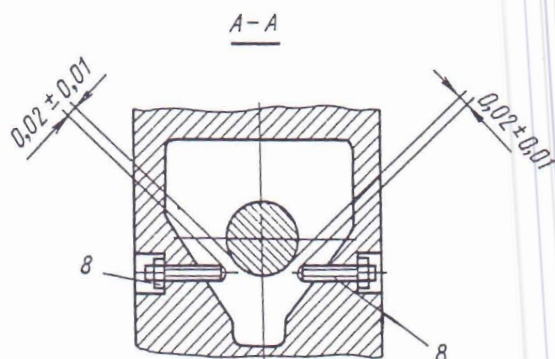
Шпиндель шлифовальной головки станков ЗЕ711В, ЗЕ721В-I, ЗЕ721ВФ-I, ЗЕ711В-I
